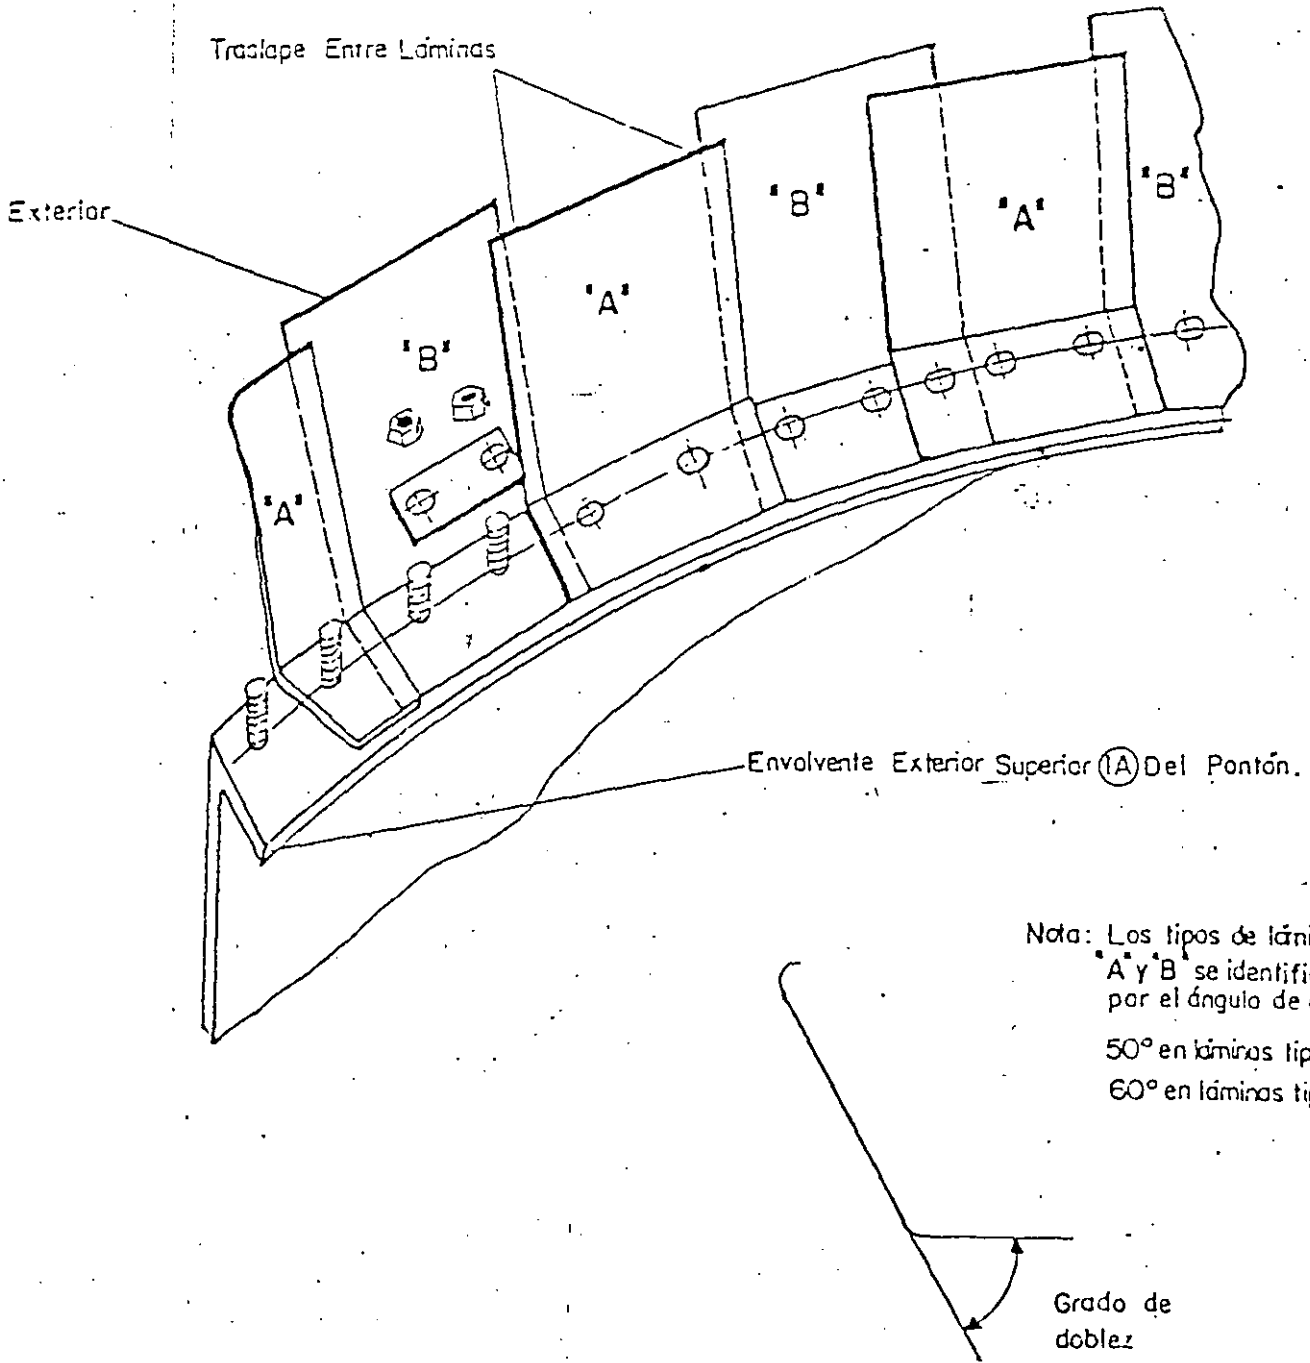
C DETALLE DE COLOCACION DE LAMINAS DE PROTECCION TIPO 'A' y 'B'
